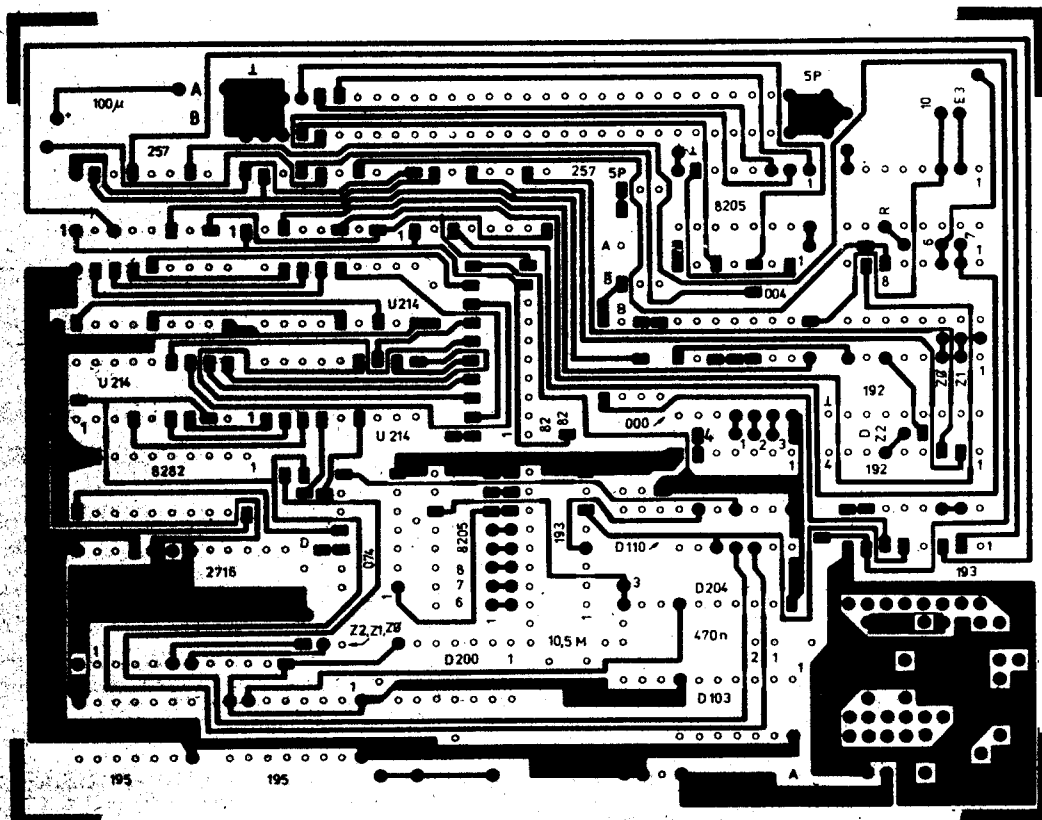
Layout der Bestückungsseite der Platine für die Bildschirmansteuerung
